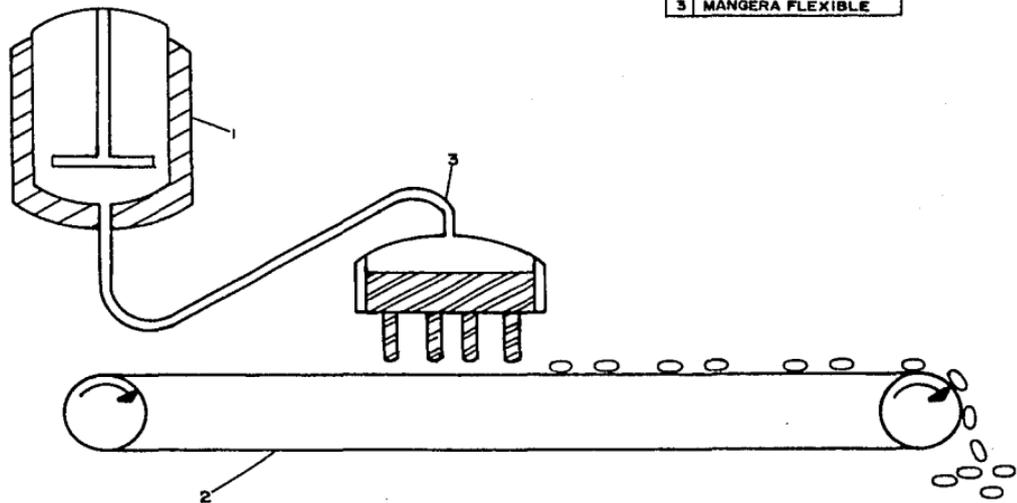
PROCESO DE PRODUCCION DE AYRTFC CON PASTILLADOR
